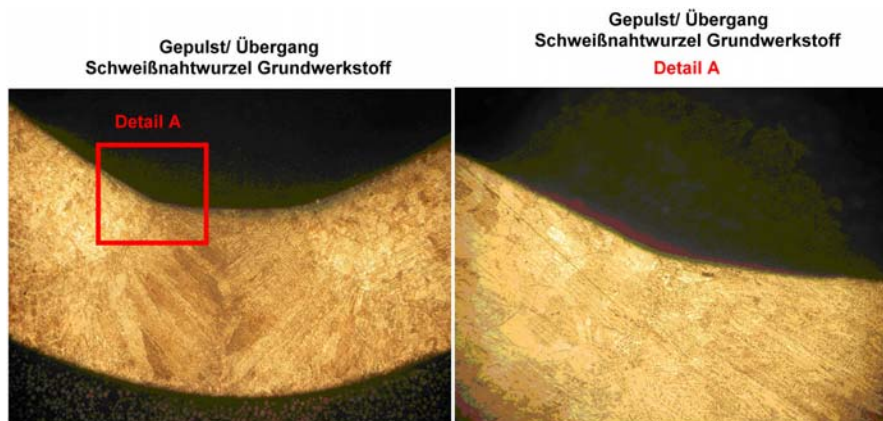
Schweißnahtgeometrie mittels WIG-Puls geschweißter Rohre
